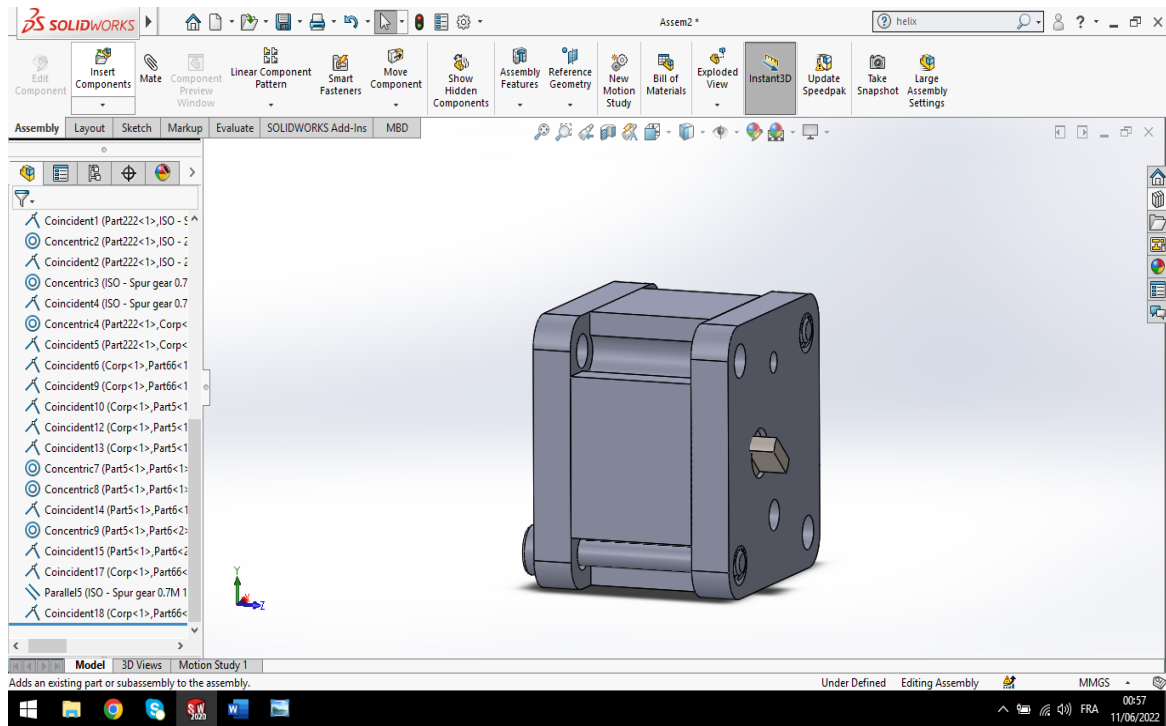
L'assemblage de la pompe à engrenages exterior à dentures droites
